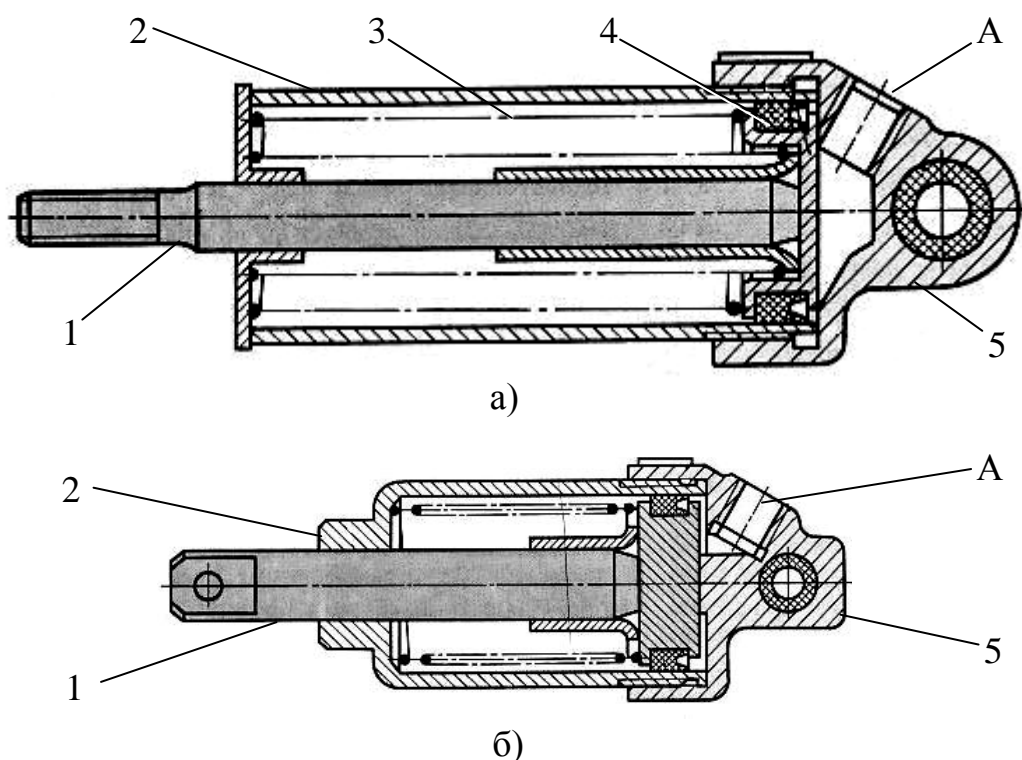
Конструкция пневмоцилиндров привода вспомогательной тормозной системы грузового автомобиля-тягача КАМАЗ: а – пневмоцилиндр привода вспомогательного тормозного механизма (заслонки во впускном коллекторе), б – пневмоцилиндр привода рычага останова двигателя; 1 – шток; 2 – корпус цилиндра; 3 – пружина; 4 – поршень; 5 – крышка цилиндра; А – вывод к крану вспомогательного тормозного механизма
